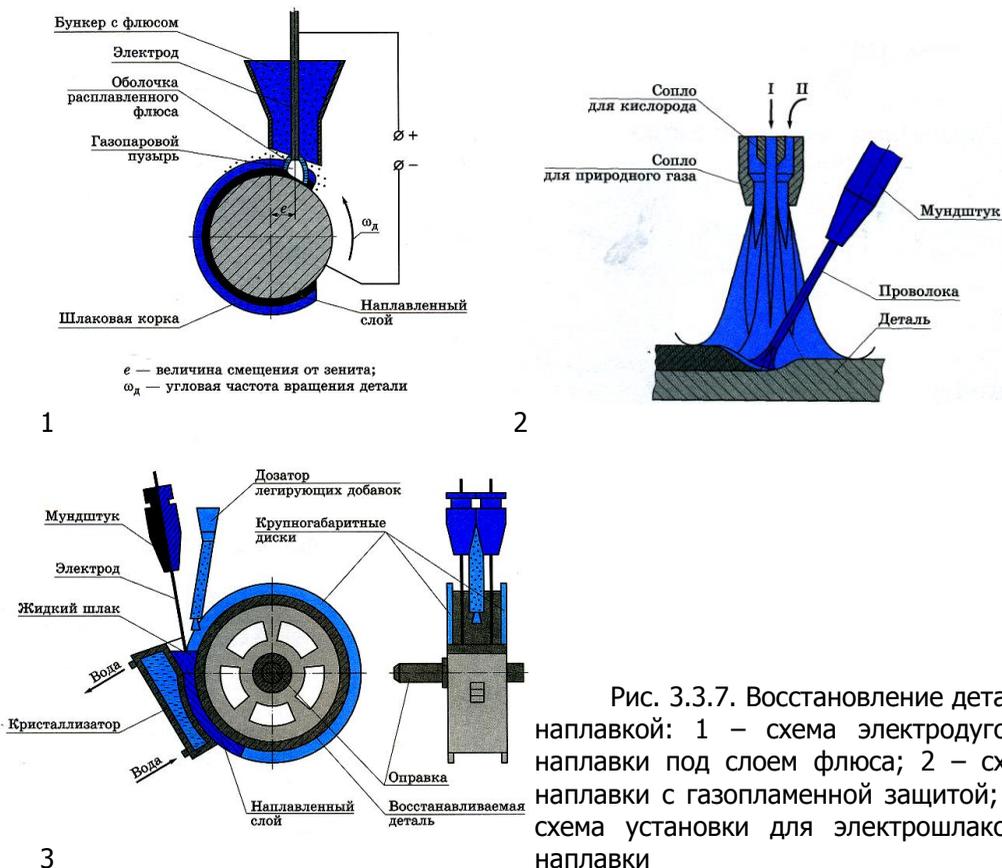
Восстановление деталей наплавкой: 1 – схема электродуговой наплавки под слоем флюса; 2 – схема наплавки с газопламенной защитой; 3 – схема установки для электрошлаковой наплавки
